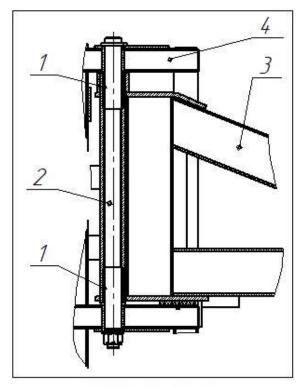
Рычаг боковой 1 – Втулка; 2 – Болт; 3 – Рычаг боковой; 4 – Рама центральная.
